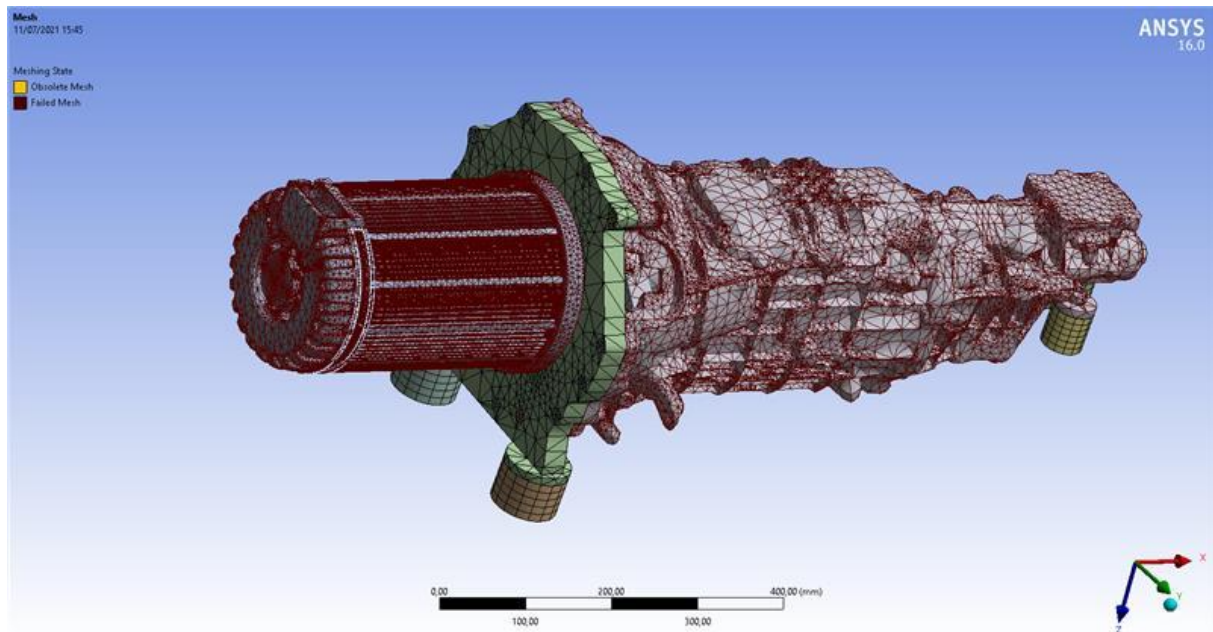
Intento de mallado del ensamblaje inicial (elaboración propia).
